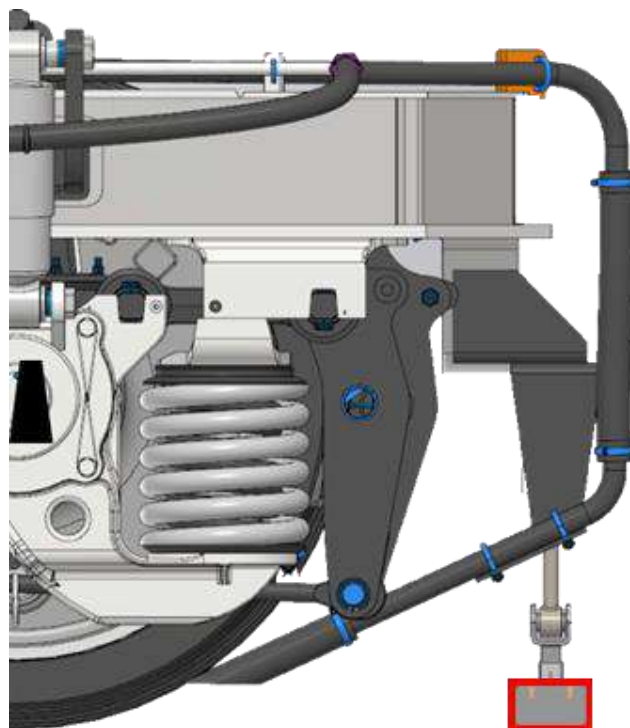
Общий вид предложенной конструктивной схемы МУКС с расположением магнитопровода перед первой колесной парой по ходу движения
